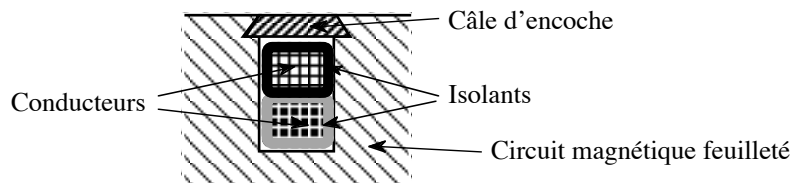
coupe d'une encoche au rotor d'une machine à courant continu.
